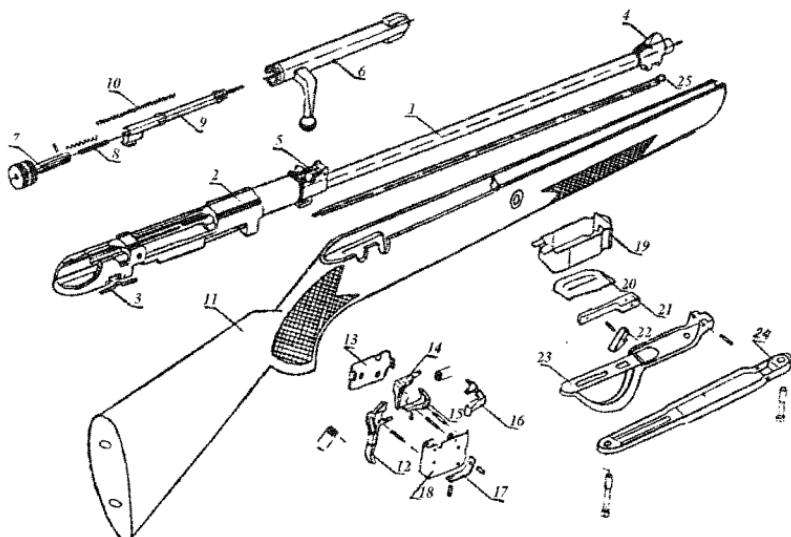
Детали карабина «Лось»: 1 - ствол; 2 - ствольная коробка; 3 - пружина предохранителя; 4 - мушка с основанием; 5 - секторный прицел; 6 - затвор; 7 - муфта затвора; 8 - указатель взведения ударника; 9 - ударник; 10 - боевая пружина; 11 - ложа; 12 - спусковой крючок; 13 - крышка спусковой коробки; 14 - шептalo; 15 - регулятор; 16 - предохранитель; 17 - дно спусковой коробки; 18 - спусковая коробка; 19 - корпус магазина; 20 - подаватель; 21 - рычаг подачи; 22 - защелка; 23 - предохранительная скоба; 24 - соединительная планка; 25 - шомпол.
